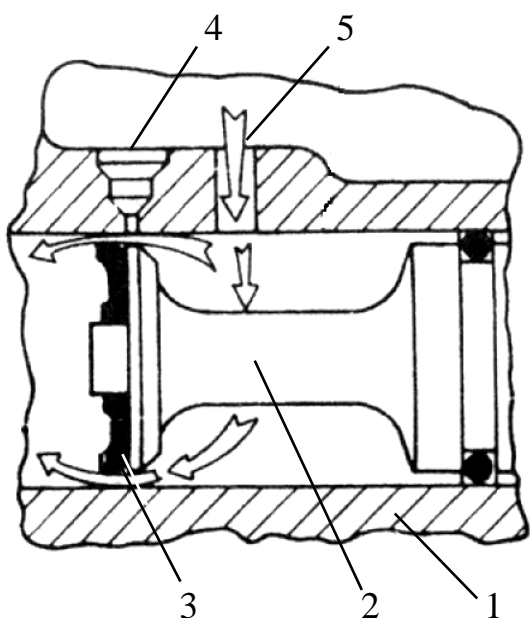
Компенсация падения давления в главном тормозном цилиндре: 1 – корпус главного тормозного цилиндра; 2 – поршень; 3 – самоподжимная уплотнительная манжета; 4 и 5 – отверстия в дополнительный бачок
